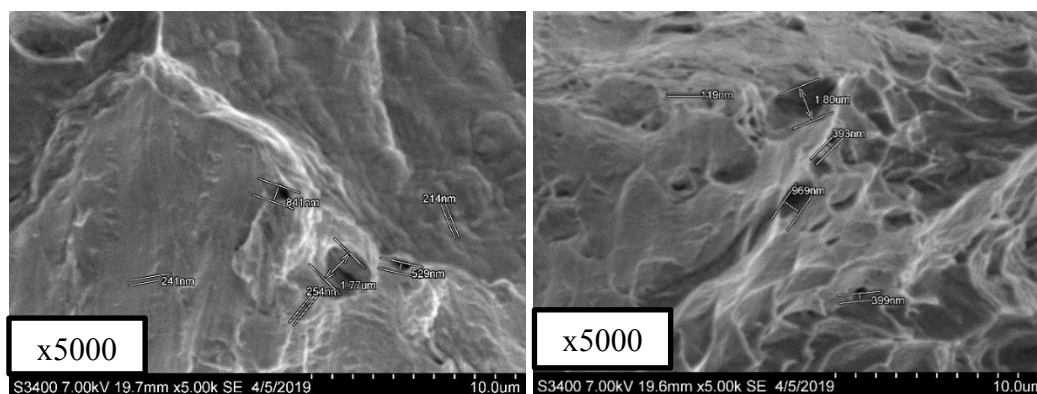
Нанопоры в изломе сварного соединения варианта 3
